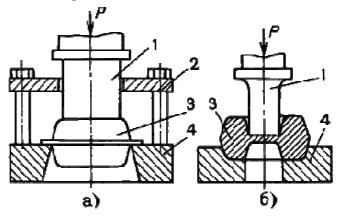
Схема обрезки заусенца и пробивки пленки 1 – пуансон, 3 – поковка, 4 – матрица.
